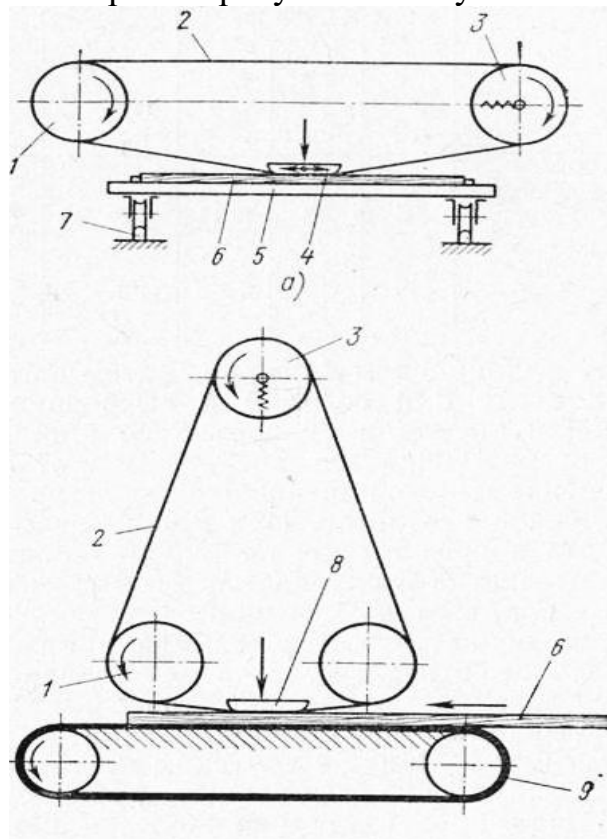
Схема шлифования заготовок на ленточных шлифовальных станках: а — с подвижным столом, б — на барабанно-ленточных; 1 — ведущий шкив, 2 — шлифовальная лента, 3 — натяжные шкивы, 4 — утюжок, 5 — стол, 6 — шлифуемая заготовка, 7 — направляющие стола, 8 — прижимная колодка, 9 — подающая лента
